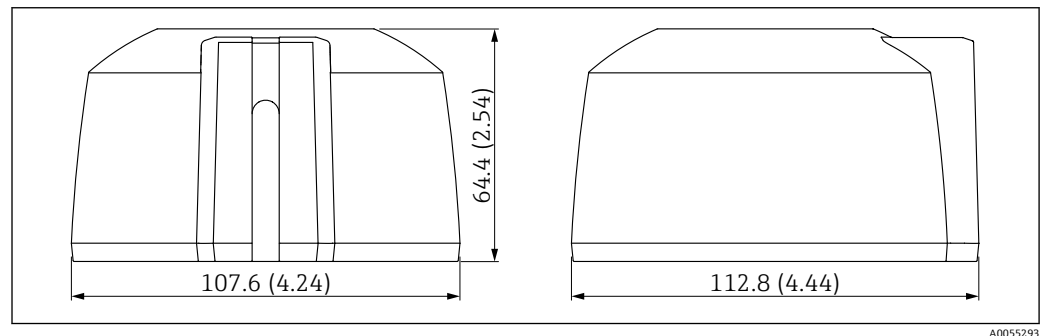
防护罩的外形尺寸（侧面电缆入口）。测量单位 mm (in)
